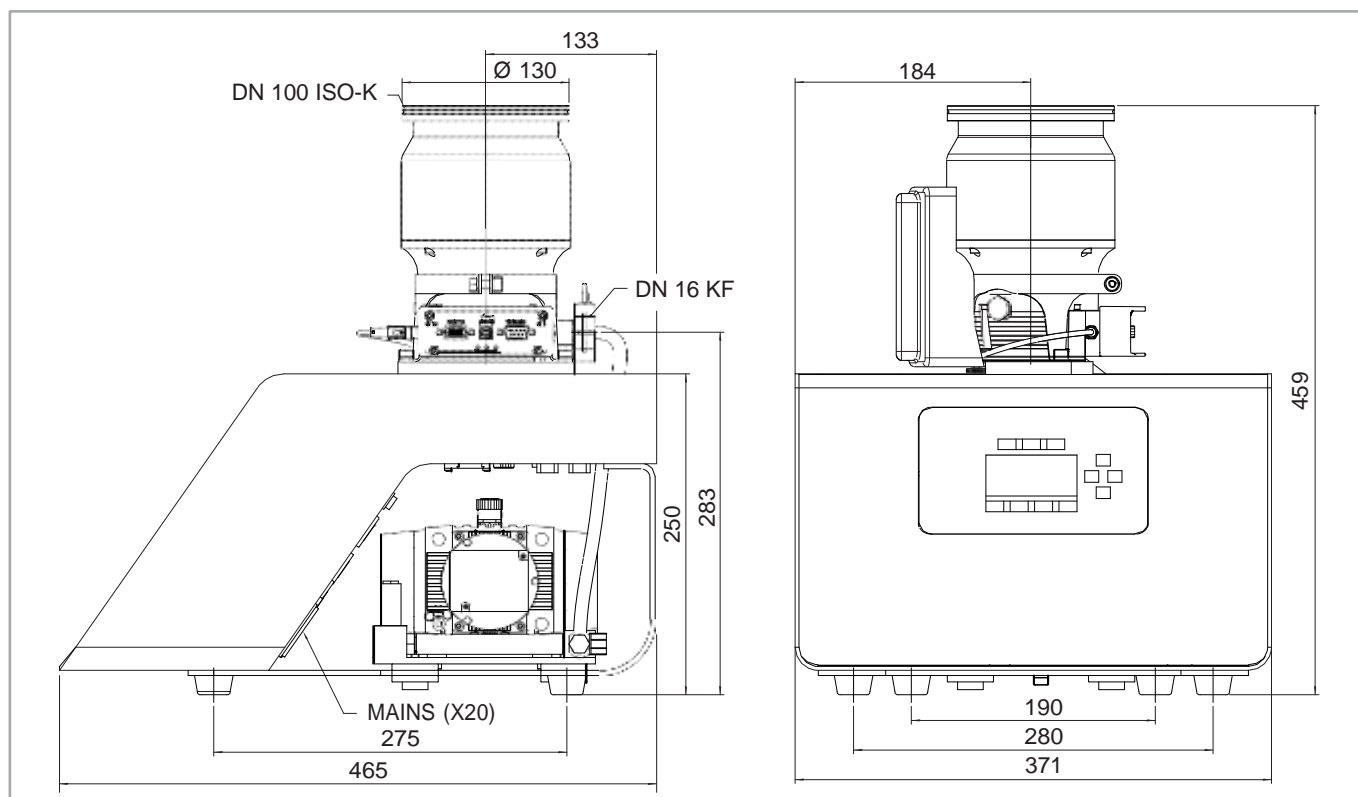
Габаритные размеры TURBOLAB 250, размеры в мм
